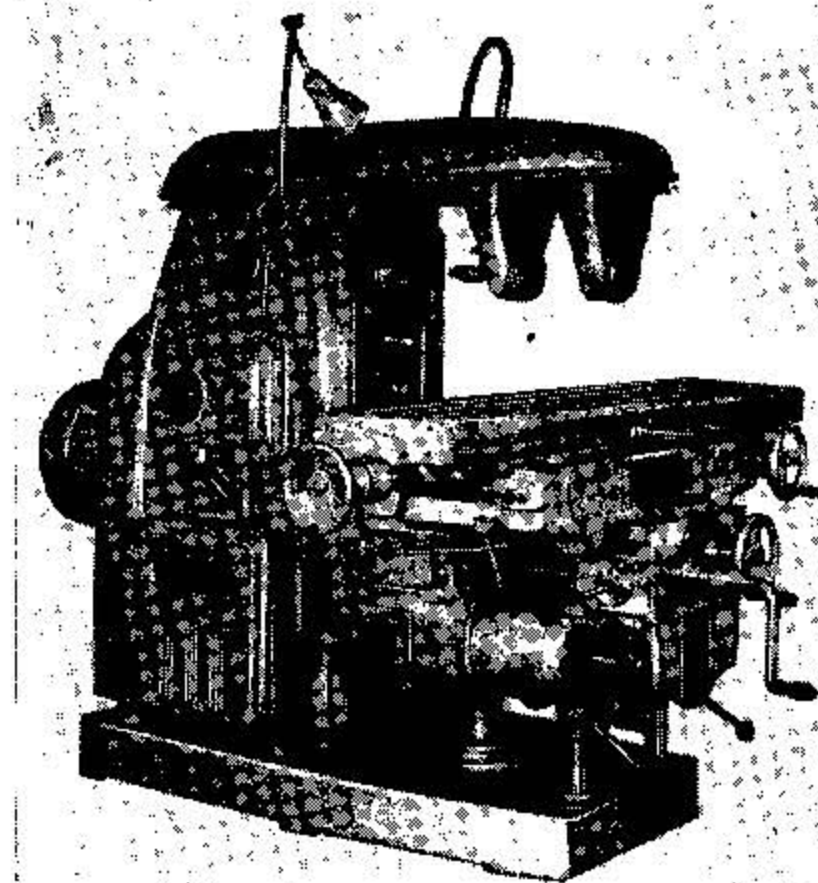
Горизонтальный консольно-фрезерный станок модели 6М83Г
